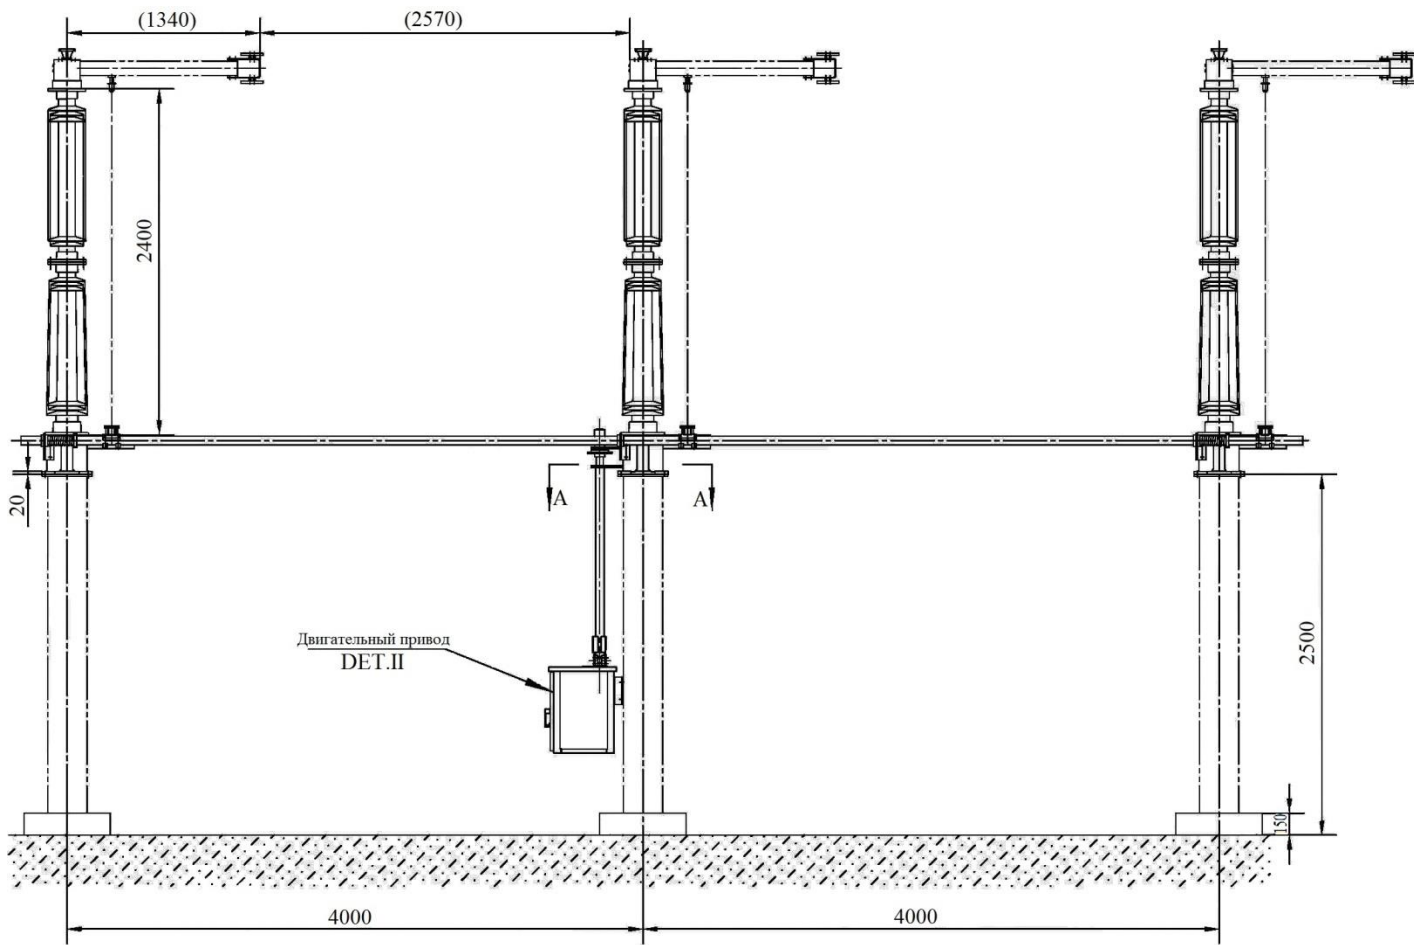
Внешний вид и габаритно-установочные размеры РГП
